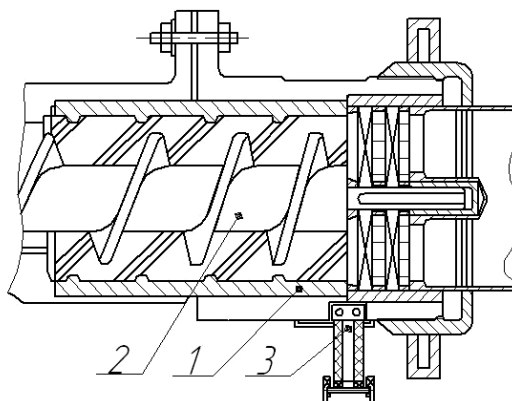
Вовчок з пристроєм для віброрізання: 1 - корпус; 2 - шнековий вал; 3 - вібропривід
